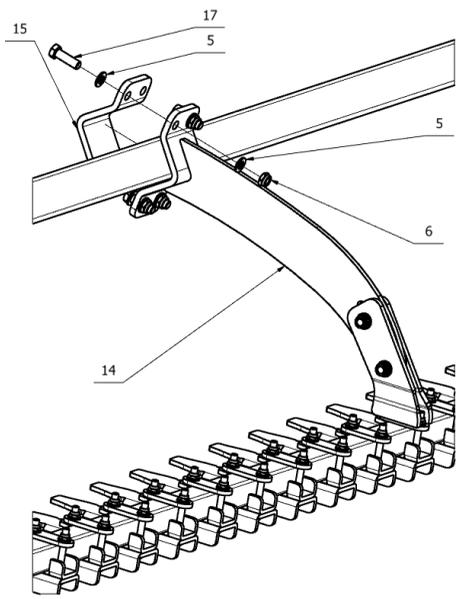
U-Profil-Walze Ø520mm – obere Befestigung der Mittelhalterung.
